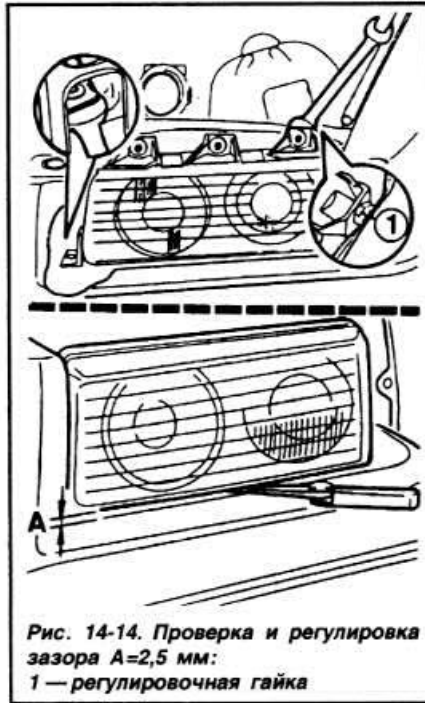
Проверка и регулировка зазора А=2,5 мм: 1 — регулировочная гайка
